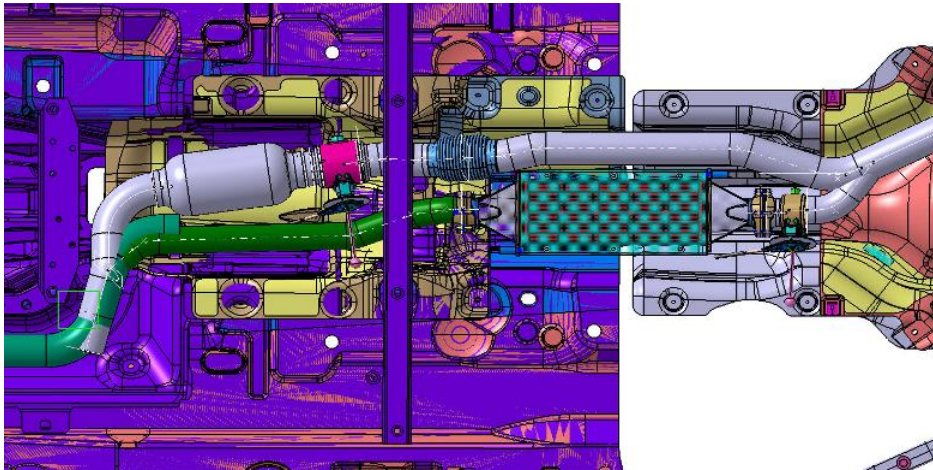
Packaging Untersuchung Fahrzeugintegration
